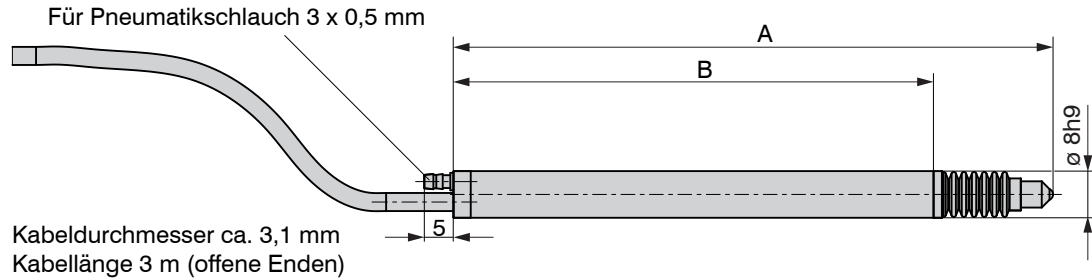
Gehäusemaße für Messtaster DTA-xG8-3-CA-V
